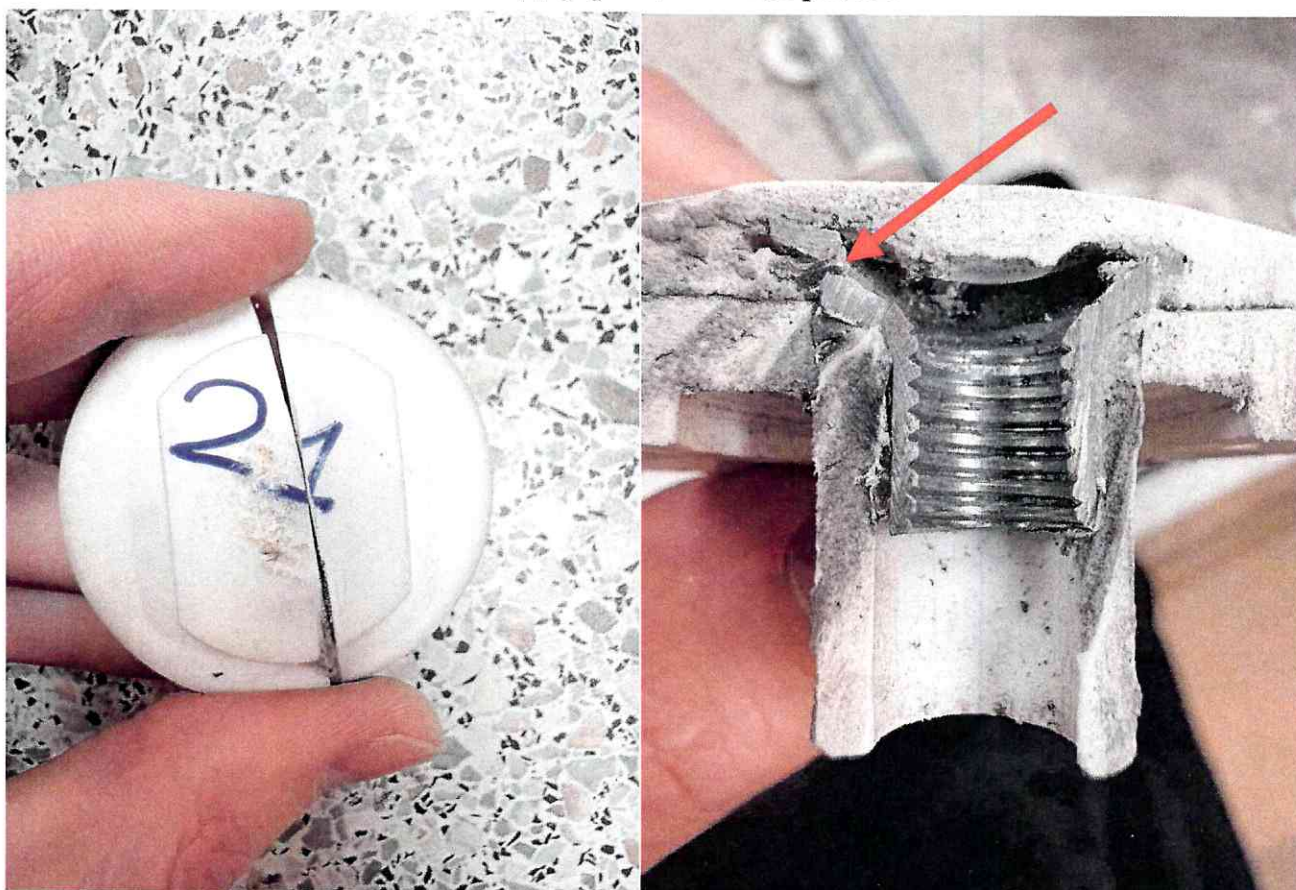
Распиленный образец 2.1, демонстрирующий разрушение опорного фланца гайки
